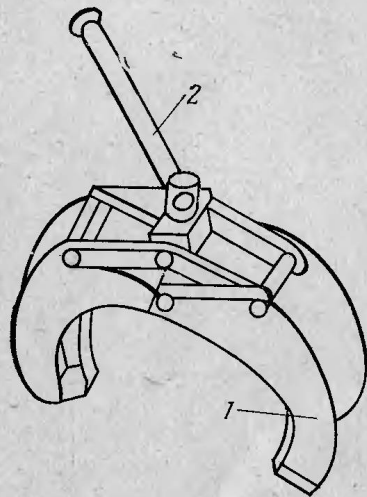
Приспособление для стыковки труб под сварку.
